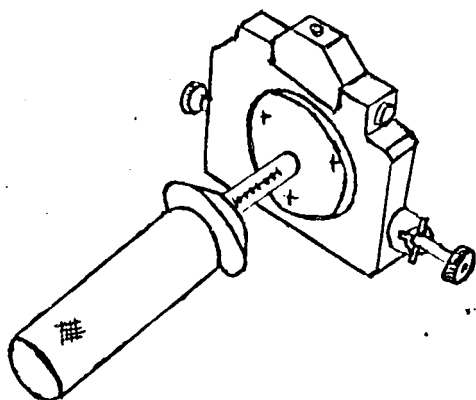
Общий вид держателя для заточки режущих пар машинок для стрижки животных.
